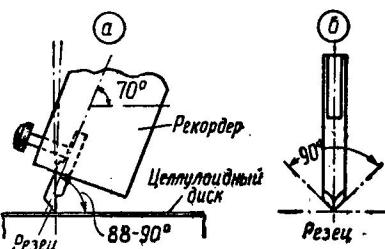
а — положение рекордера при записи; б — угол заточки резца
